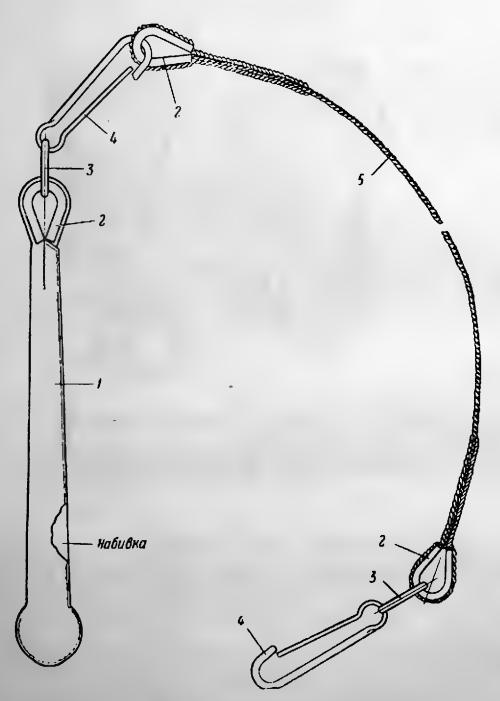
Спусковой шнур: 1 — рукоятка (С66-1); 2 — коуш (6-6); 3 — кольцо (6-2); 4 — карабин (6-1); 5 — веревка (6-3)
